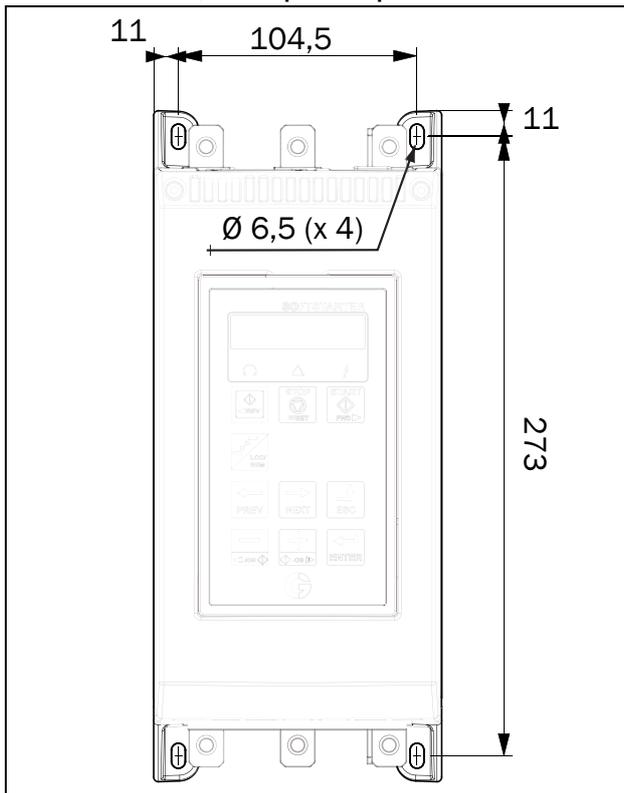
Расположение отверстий Emotron TSA, типоразмеры 1 и 2.
